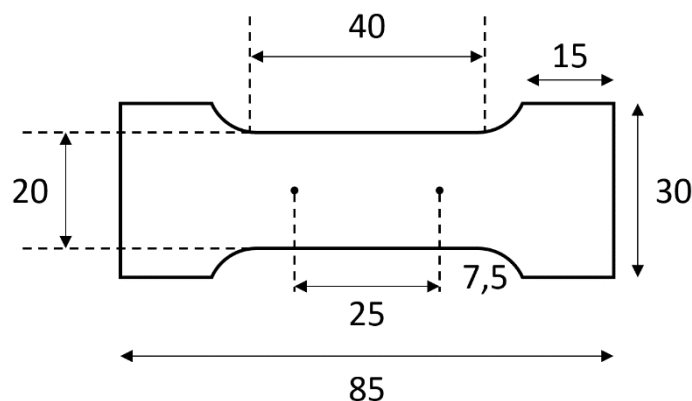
Dimensions (mm) des éprouvettes de traction
